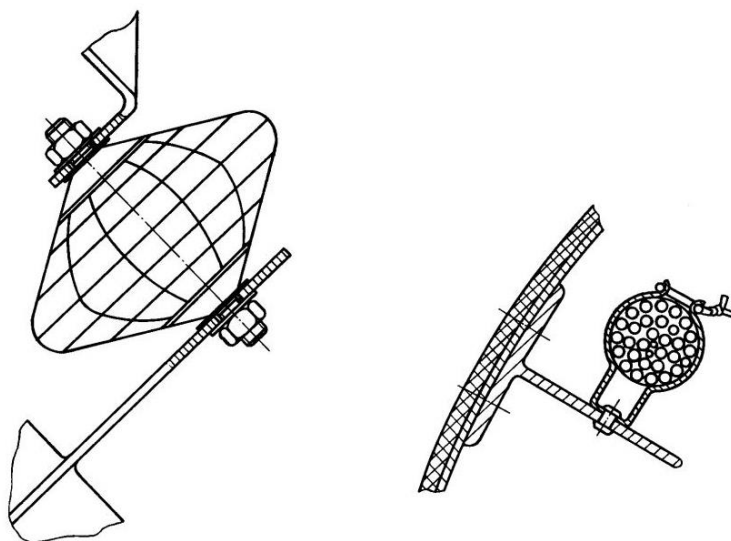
а) – кріплення приладів; б) – кріплення кабелів.
